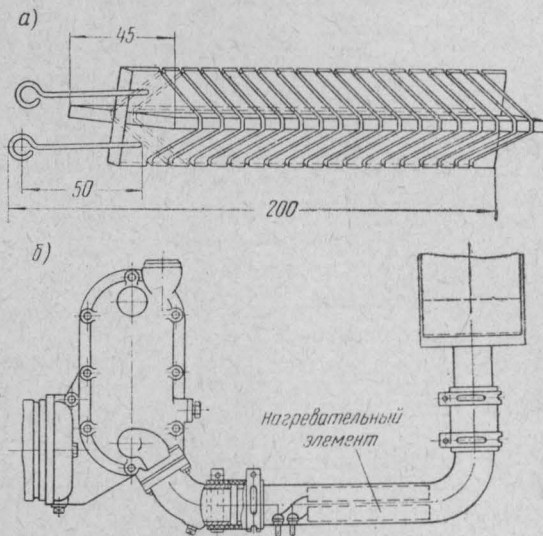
Электронагревательный элемент с открытой спиралью для двигателя ЯАЗ-204: а — нагревательный элемент; б — размещение элемента.
